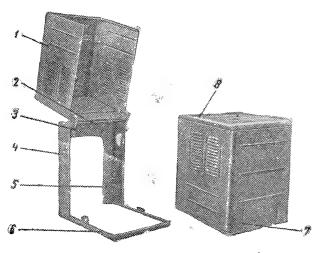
Қожух: I — подвижная часть; 2 — прокладка; 3 — система рычагов; 4 — неподвижная часть; 5 — отверстие для крепления кожуха на блоке аппаратуры; 6 — отверстие для крепления кожуха на опоре двигателя; 7 — натяжной замок; 8 — отверстие для заливки бензина в топливный бак
